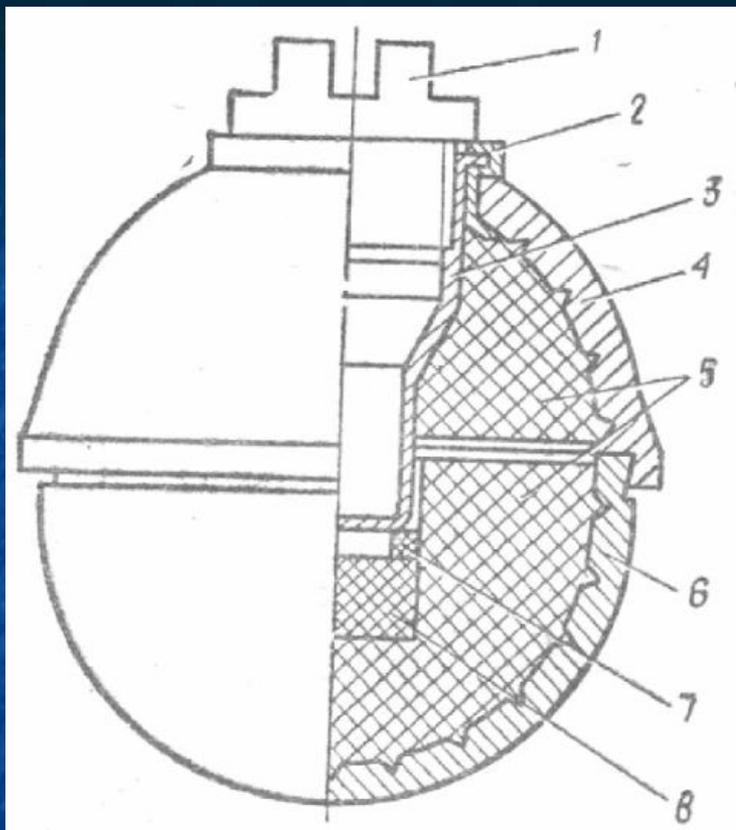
Устройство ручной гранаты РГН без запала: 1 – пробка; 2 – манжета; 3 – стакан; 4 – полусфера; 5 – взрывчатая смесь; 6 – полусфера; 7 – прокладка; 8 – шашка
